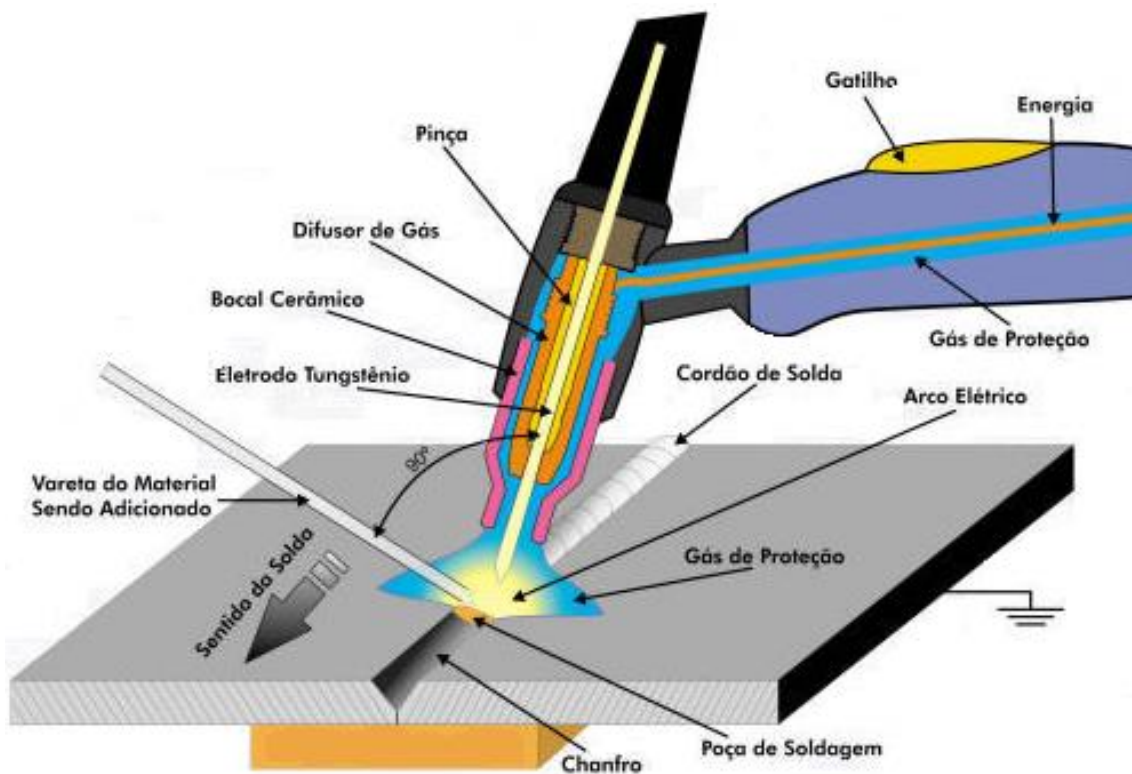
Esquema representativo da soldagem TIG com corte da tocha de soldagem [Adaptado de DCB Oxigênio, 2013].
